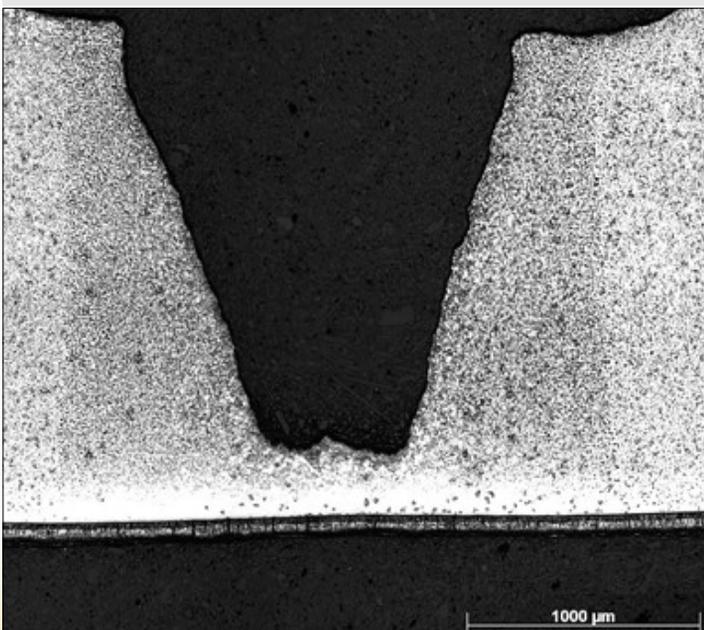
détail de la coupe. On voit bien l'attaque préférentielle au milieu de la soudure
